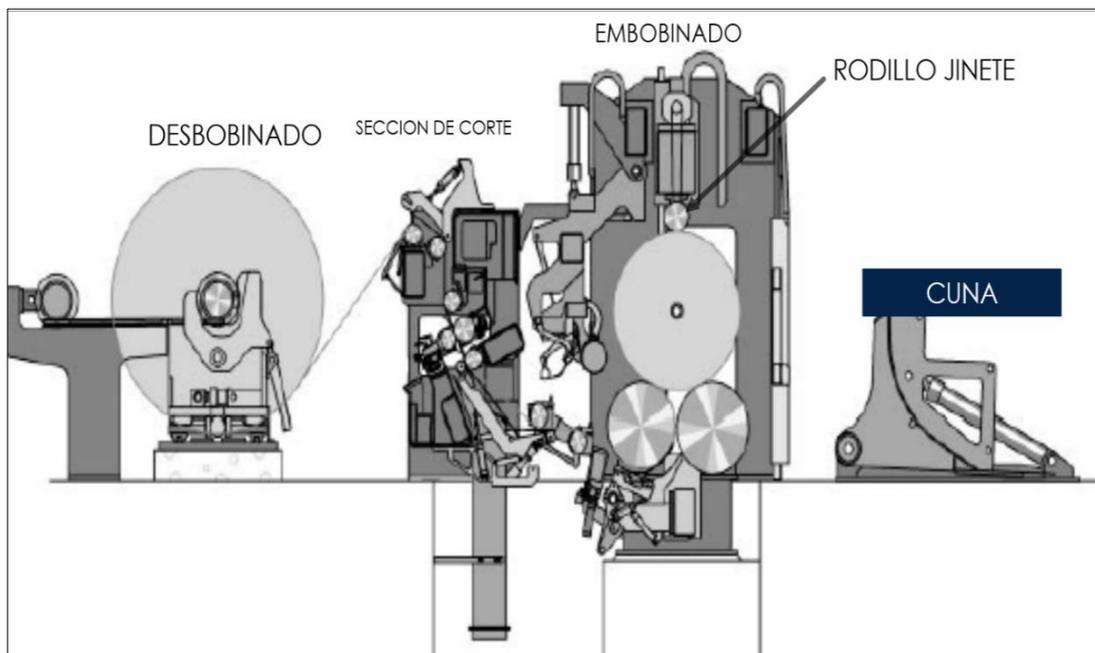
Vista General Máquina Bobinadora de Dos Tambores.
